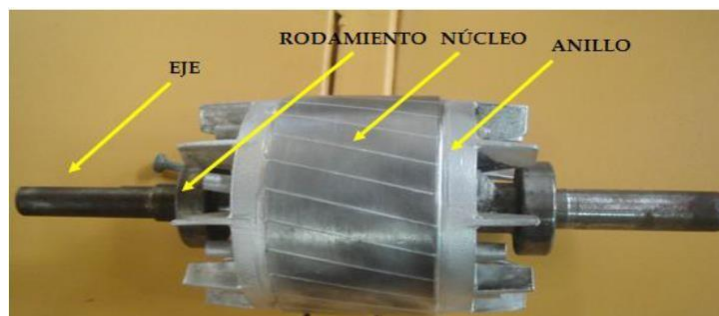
Partes principales del rotor de bobinado Fuente: Francisco, Cánovas & Molina, 2011.
